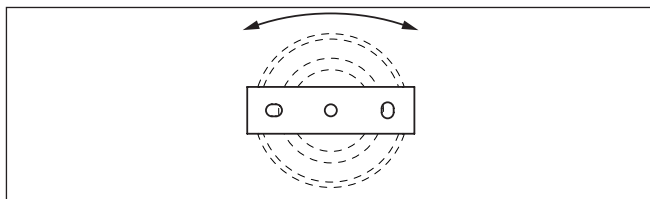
Rotazione in caso di montaggio in posizione verticale sul soffitto/cielo
